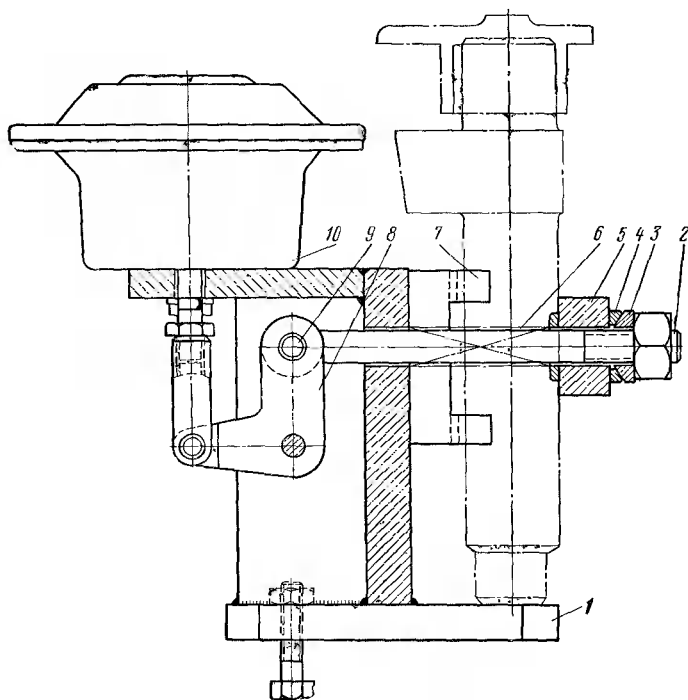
Приспособление для сборки сектора с крышкой рулевого механизма:
